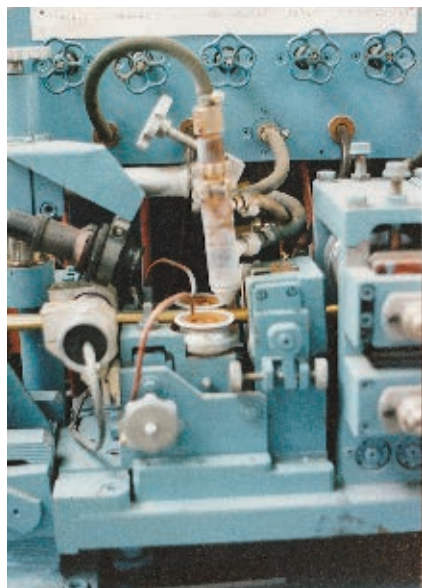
Узел сварки (камера вытяжки газов снята) стана АДСТ 5...25-1К левого исполнения, датчик теплового потока (слева), над ним — оптический прибор для вывода изображения зоны сварки на экран дисплея
